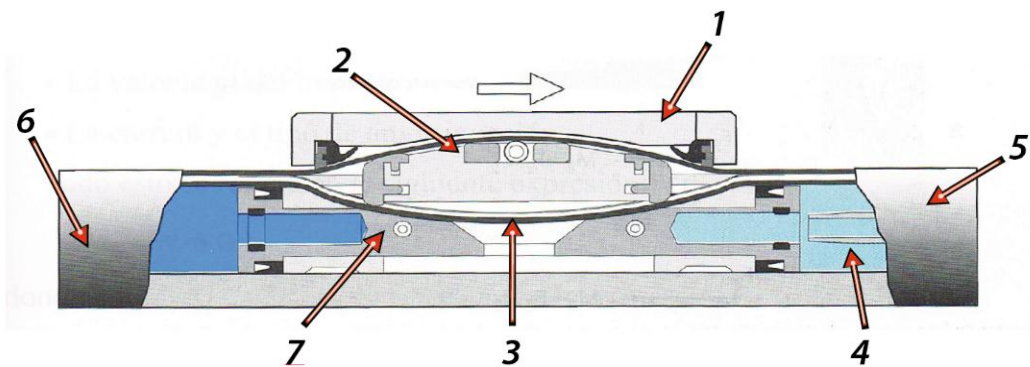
Cilindro sin vástago de transmisión mecánica.
